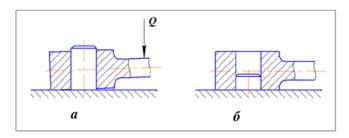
Установка заготовки по торцу и отверстию: а — неправильное базирование; б — правильное базирование
